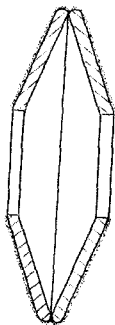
Абразивный инструмент из двух тарельчатых пружин, образующих O-образный профиль.
